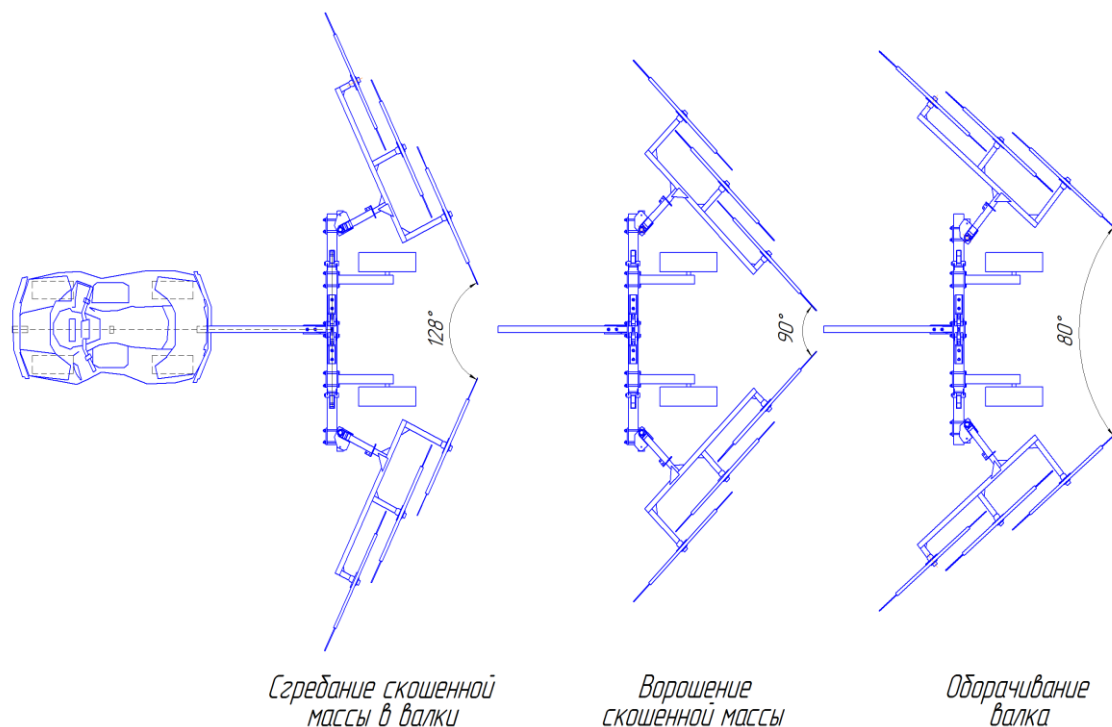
Схема установки рабочих колёс граблей для мотовездехода
